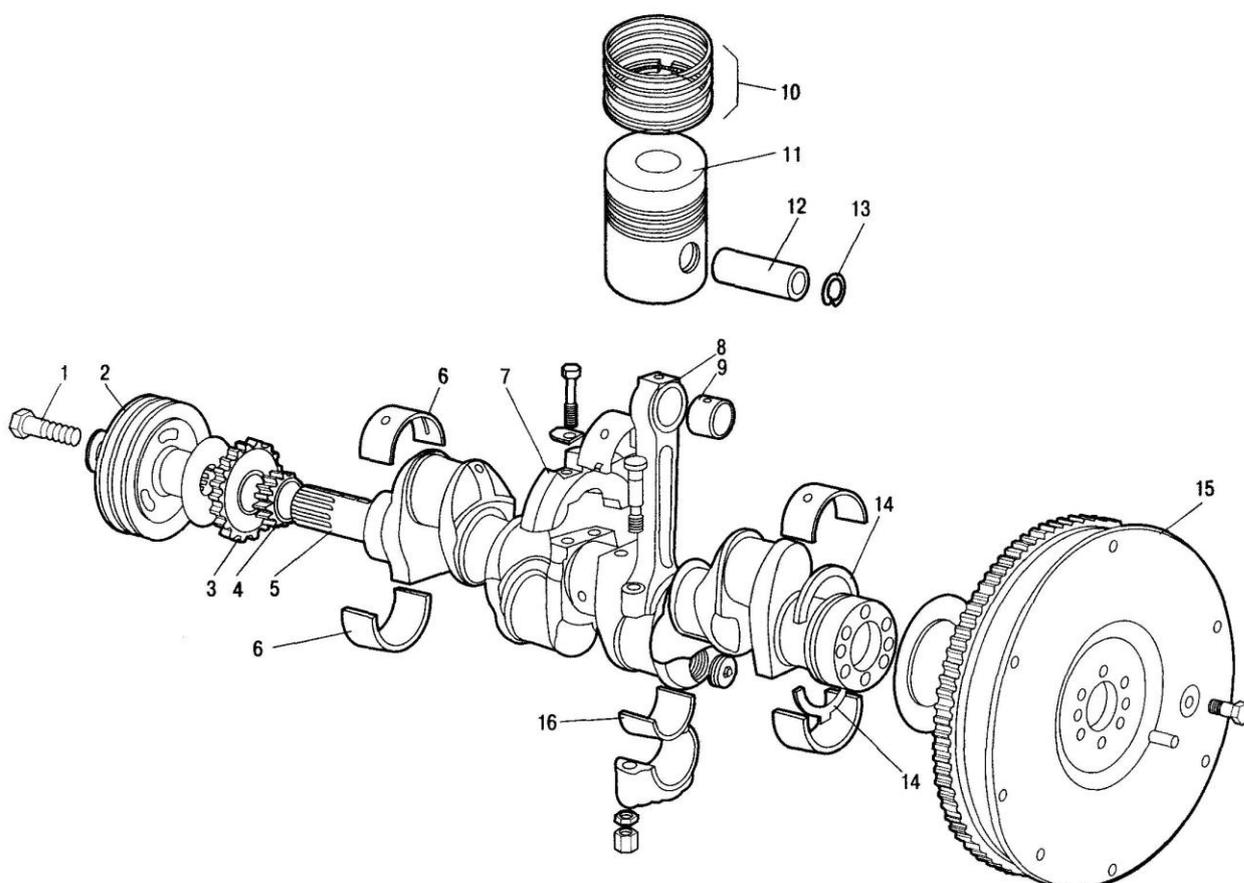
Кривошипно-шатунный механизм: 1 - болт; 2 - шкив коленчатого вала; 3 - шестерня привода масляного насоса; 4 - шестерня привода; 5 - коленчатый вал; 6 - вкладыши коренной шейки; 7 - противовес; 8 - шатун; 9 - втулка шатуна; 10 - поршневые кольца; 11 - поршень; 12 - палец; 13 - стопорное кольцо; 14 - полукольца; 15 - маховик; 16 - вкладыши шатунной шейки
